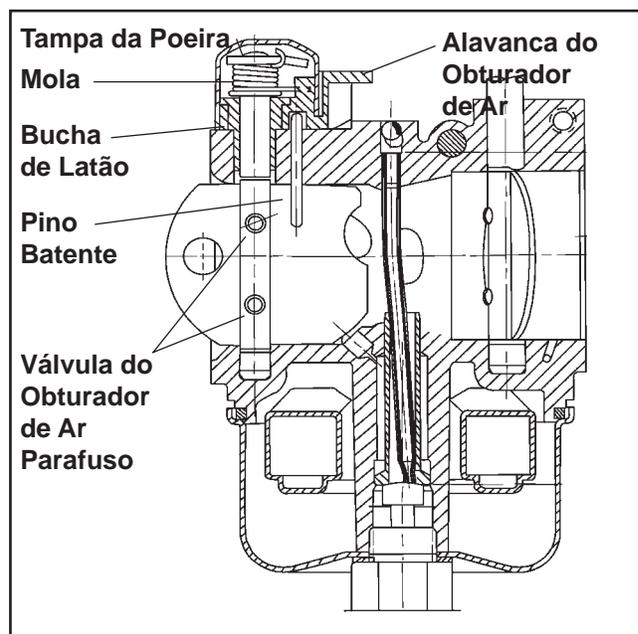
Vista de Corte Mostrando o Carburador da Placa do Obturador de Ar de Auto-Libertação.
